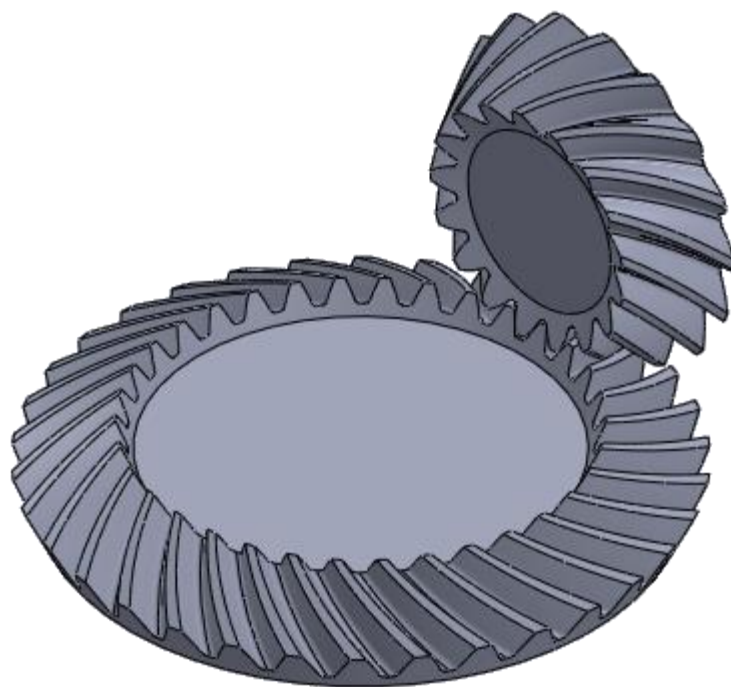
Par de engranajes cónicos espirales. Fuente Autor
